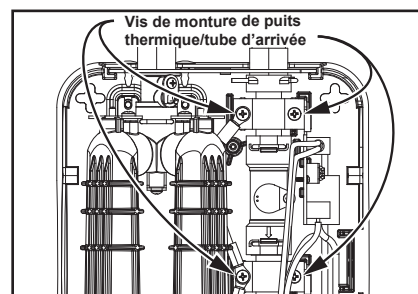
Vis de montage de puits thermique/tube d'arrivée.
